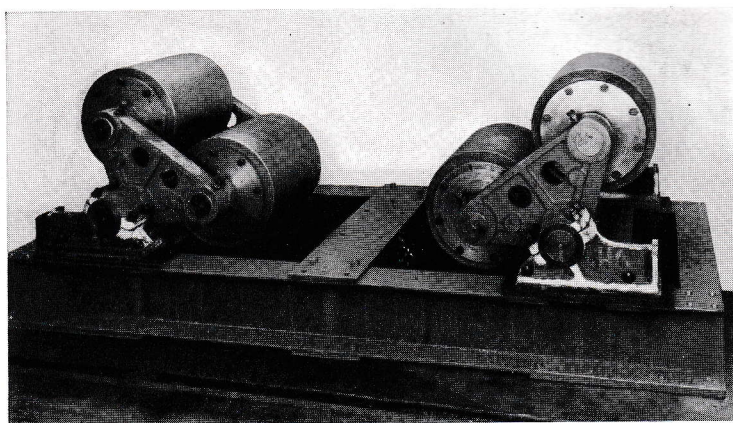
Rodillos de apoyo para el tambor lavador de mineral
